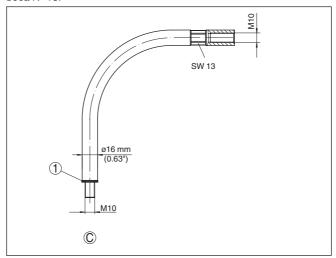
Componentes de varilla y cable - ø 16 mm (0.63 in)
